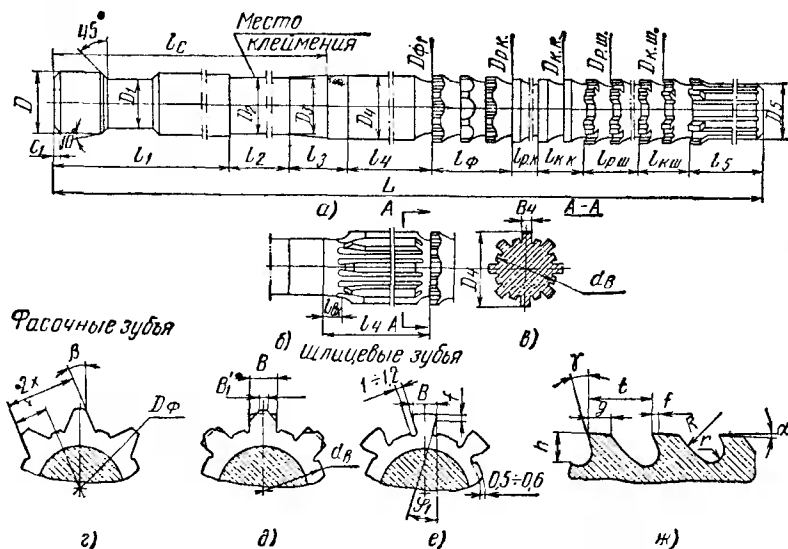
Конструкция и обозначения параметров шлицевой протяжки: а — общий вид протяжки первого прохода, б — передняя направляющая часть протяжки второго прохода, в — сечение по передней направляющей части, г — поперечный профиль фасочных зубьев, д — поперечный профиль режущих шлицевых зубьев, е — поперечный профиль калибрующих шлицевых зубьев, ж — продольный профиль зубьев
